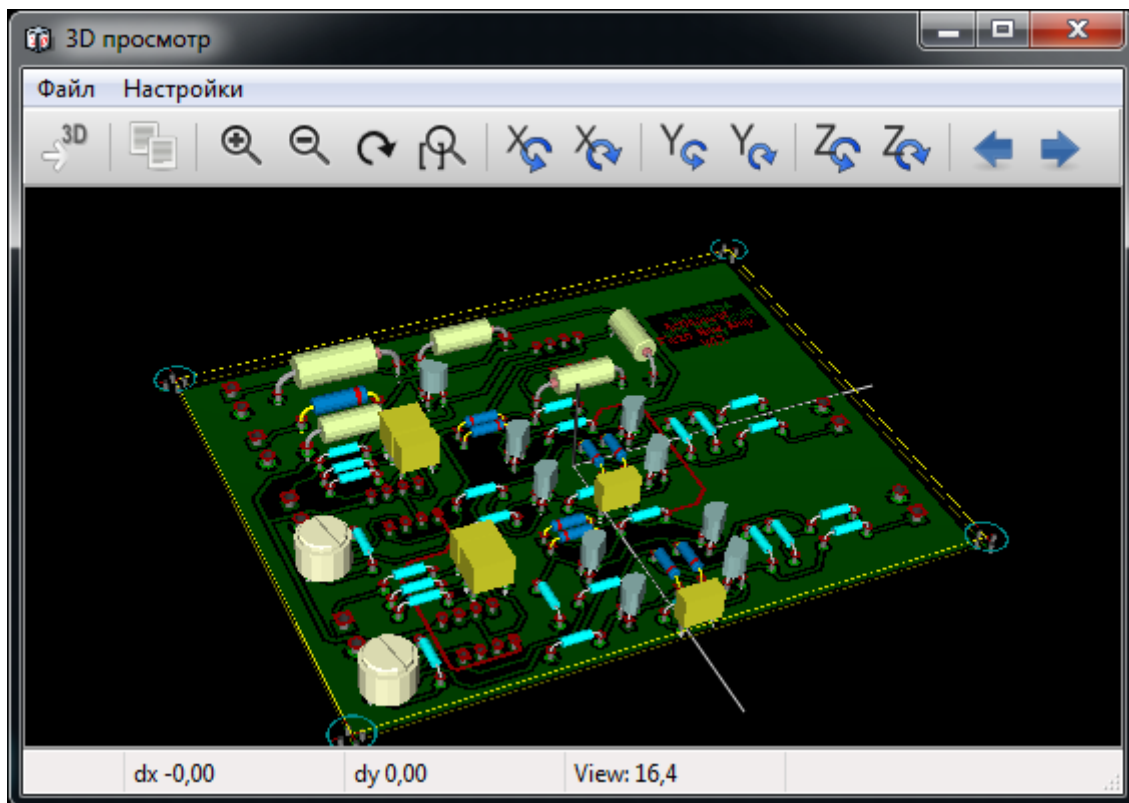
3D-просмотрщик печатных плат на базе OpenGL (часть Pcbnew) 3D Viewer
